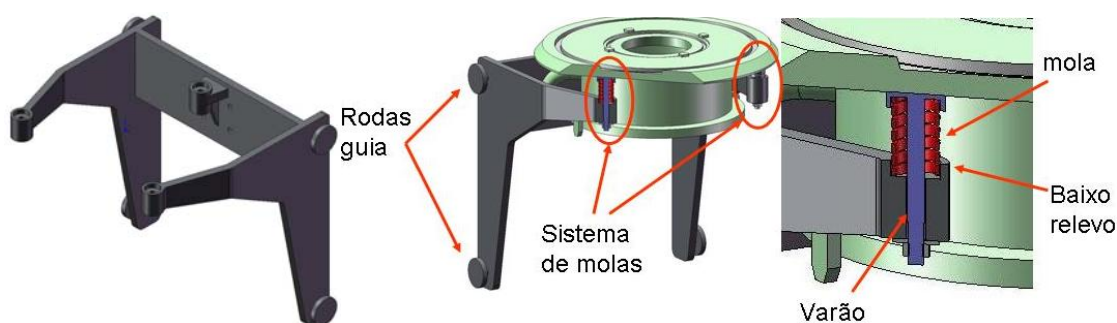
Estrutura de apoio da câmara de vazamento. Sistema de fixação da câmara de vazamento superior à estrutura que a suporta. Pormenor da montagem da mola.
